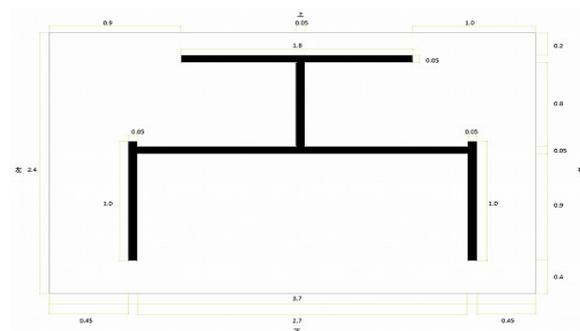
マット上側の裏面の設計図 (m)
